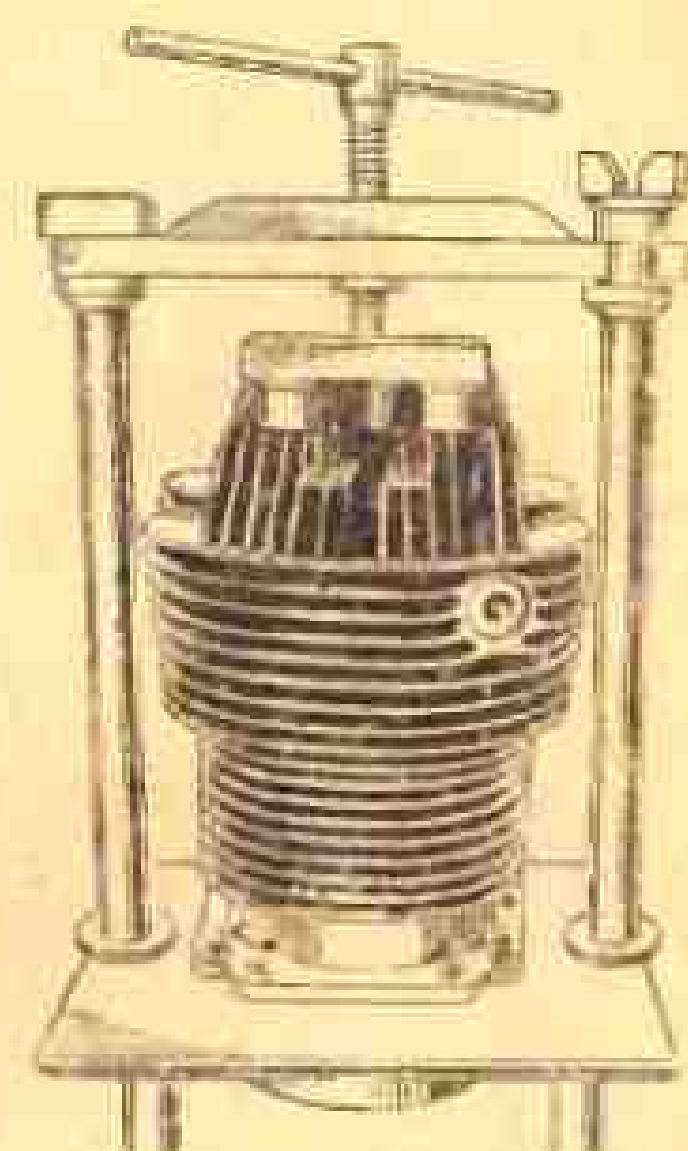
Приспособление для запрессовки втулок клапанов коварно
